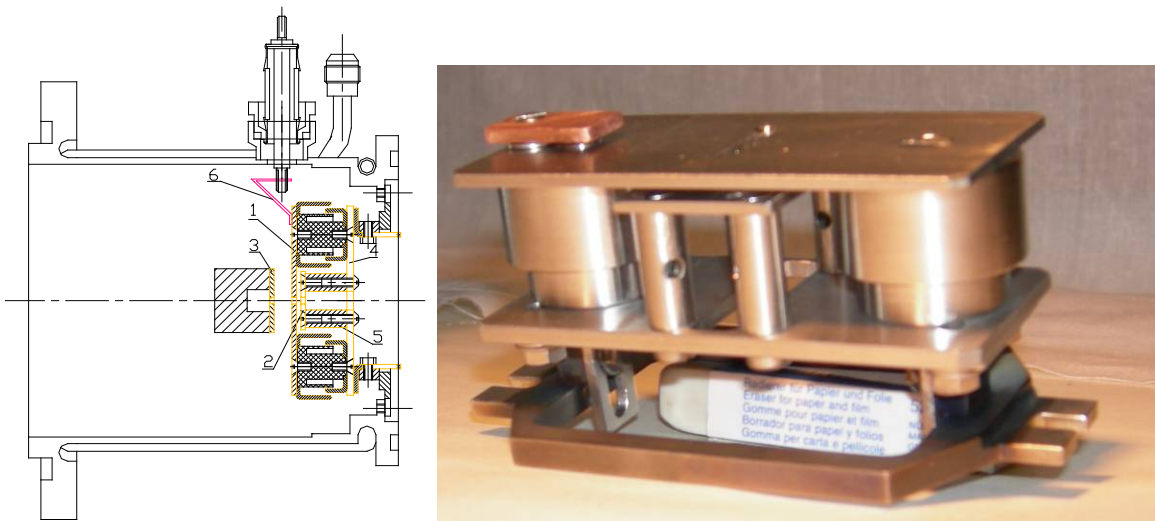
Конструкция и сборка новой формирующей оптики:
